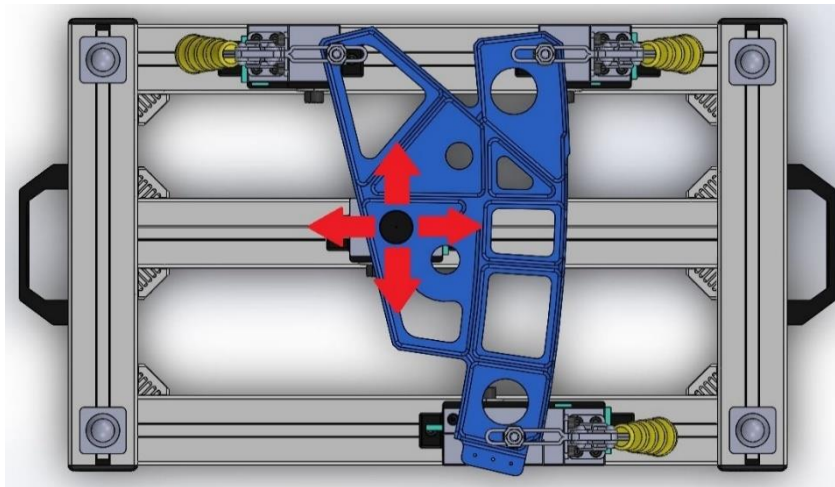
Konstrukční řešení pružného elementu [29]
